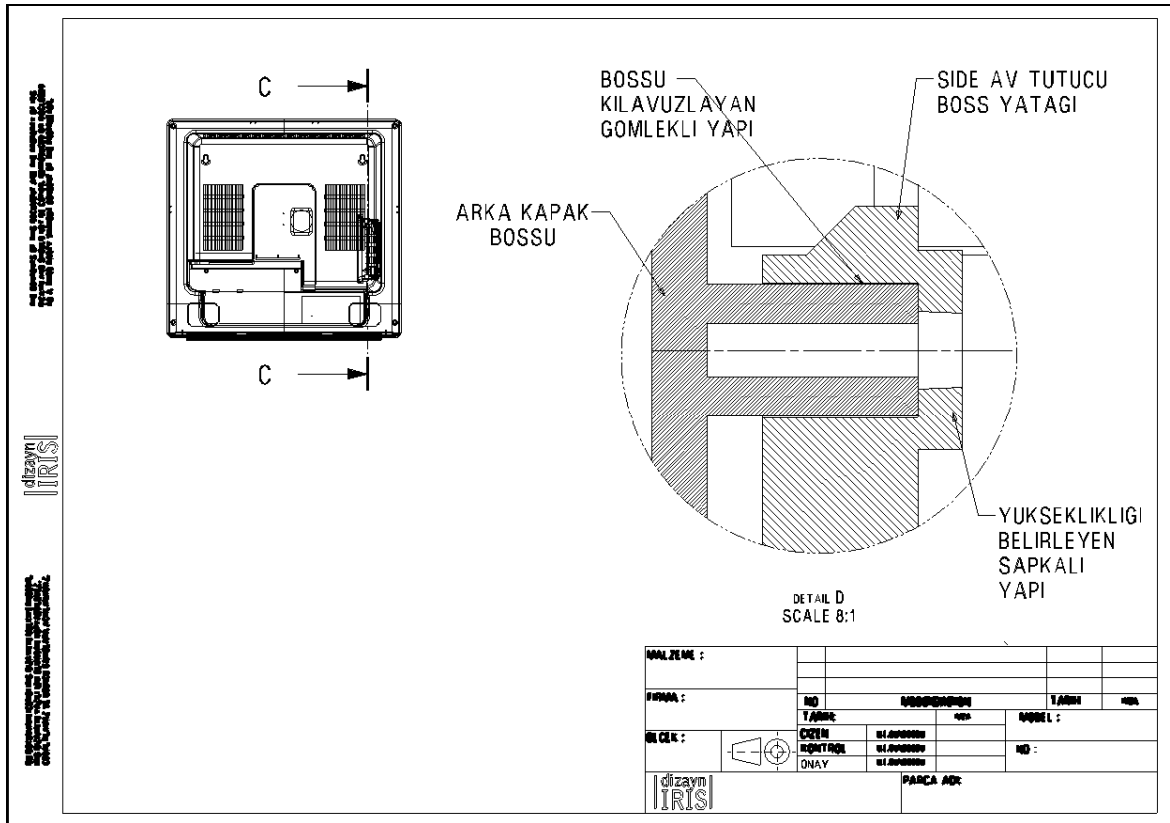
53 Side AV PCB montaj deliklerinin tasarımı
